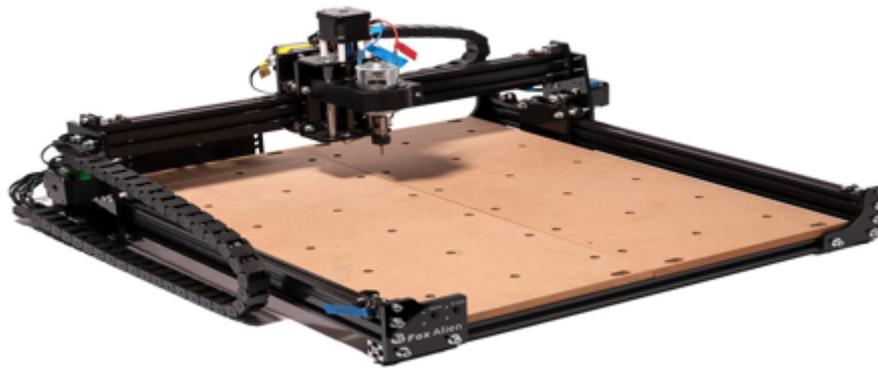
Exemple de machine CNC à 03 axes. [16]
